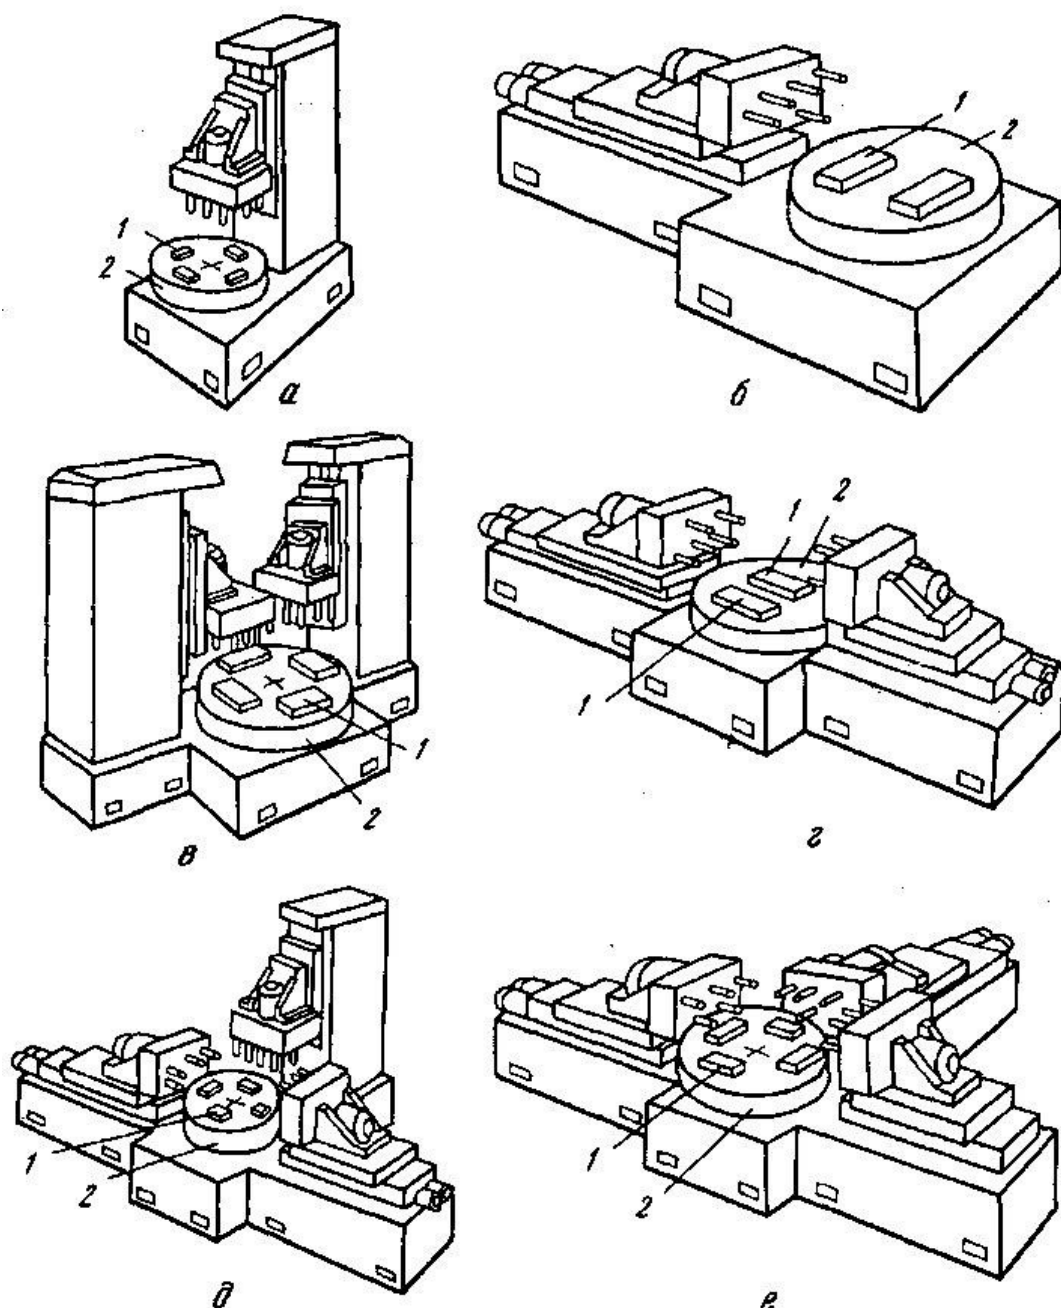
Типові компоновки агрегатних верстатів з поворотним ділильним столом
